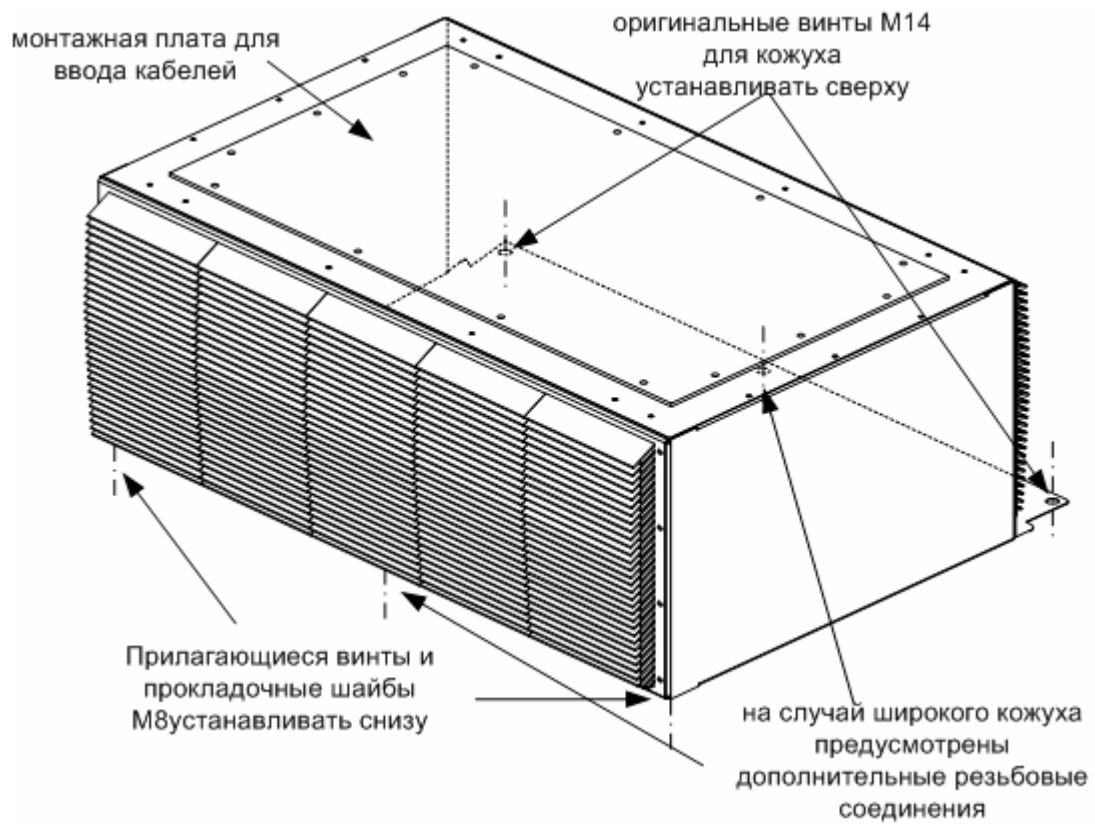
Монтаж колпака крышки для M13 / M78
